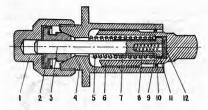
Натажитель цепи: 1.— фиксирующая тайка; 2.— зажимной сухарь; 3.— регулировочный стержень; 4.— корпус; 5.— пружина (большая); 6.— плуижер; 7.— центрирующая трубка; 8.— пружина (малая); 9.— упорная шайба; 10.— стопорное кольцо; 11.— толябка стержия; 12.— резиновый демифер.
